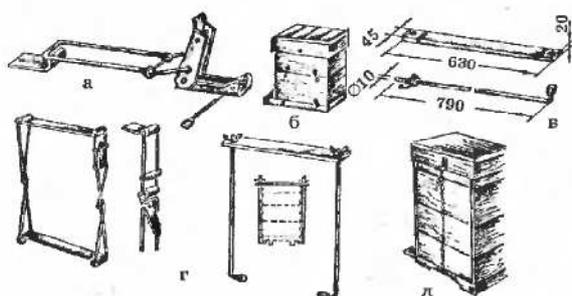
Ульевые скрепы: а — натяжной скреп; б — петля и пластинки на шурупах; в — скреп «хомут»; г — скрепы замковым соединением; д — цепные скрепы
